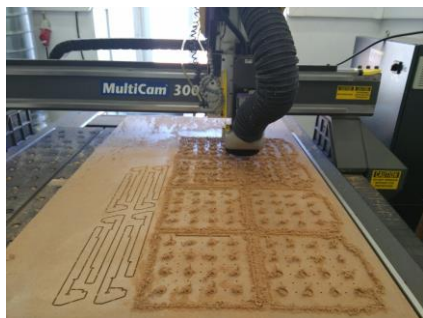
Corte do protótipo final na máquina CNC (Fonte: própria)
